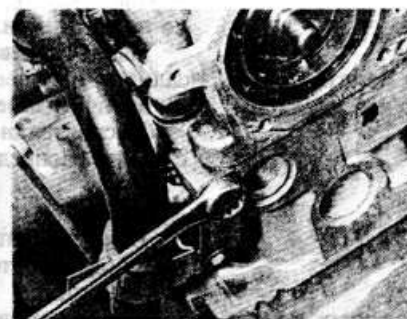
Отвинчивание болта крепления кронштейна трубы сапуна картера двигателя от головки цилиндров — двигатель 2,0 л
